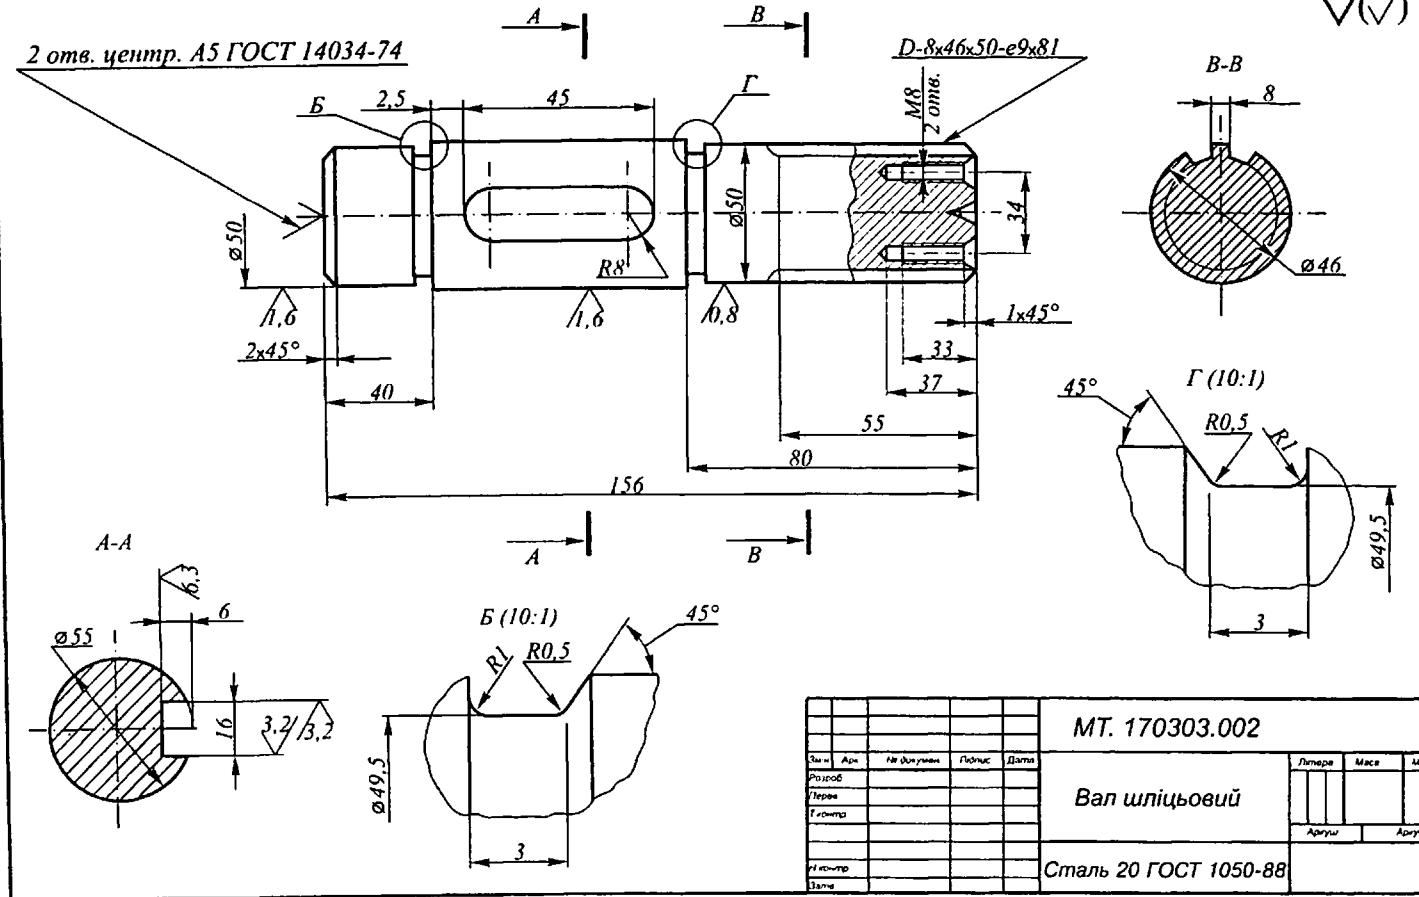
Приклад оформлення кресленника шліцьового вала
